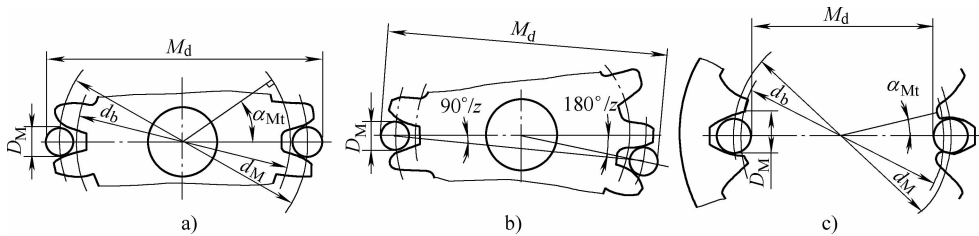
直齿轮的跨球（圆柱）尺寸  $M_d$
